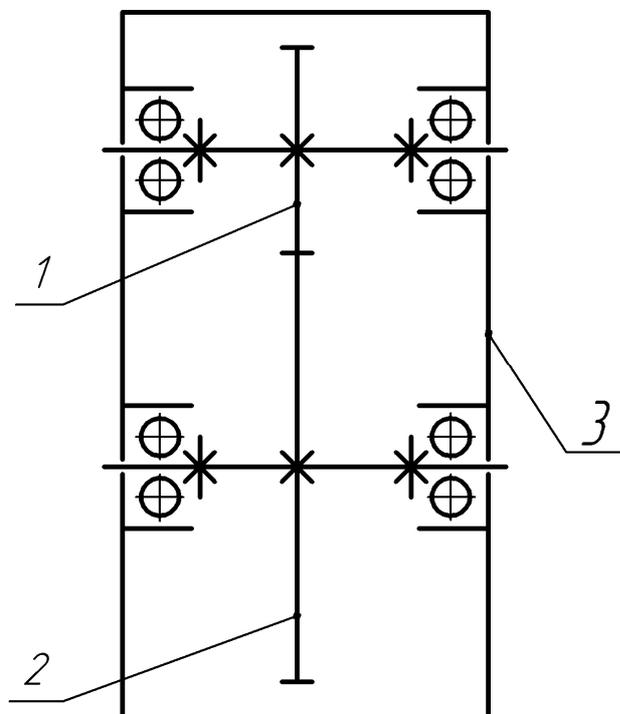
Зубчатая передача с расположением колёс между опорами.
